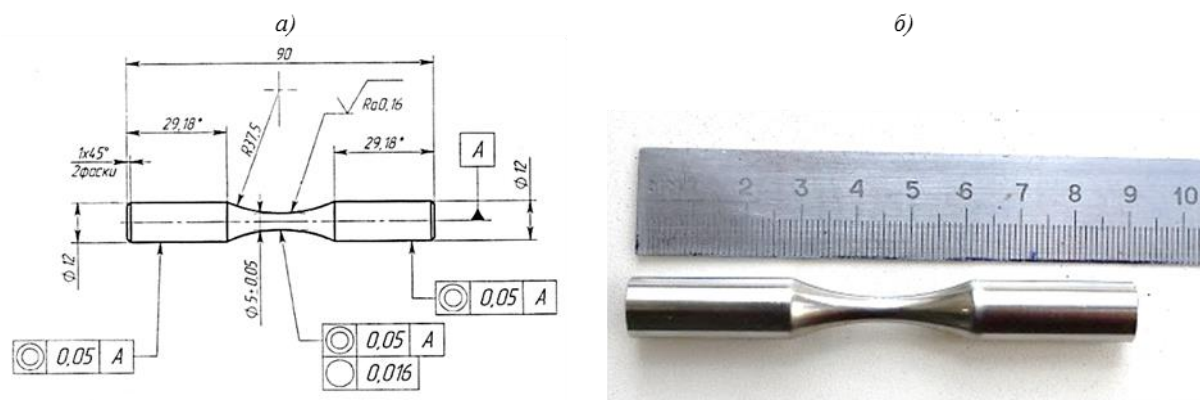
Эскиз (а) и общий вид образца (б) для испытания по схеме «чистый изгиб с вращением»
